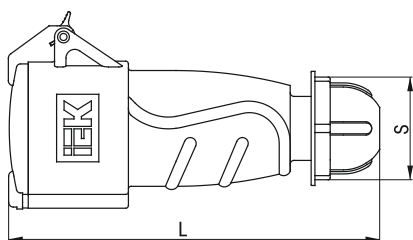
Габаритные размеры соединителей типа ССИ-045 / Figure 3 – Overall dimensions of plug and socket-outlets
